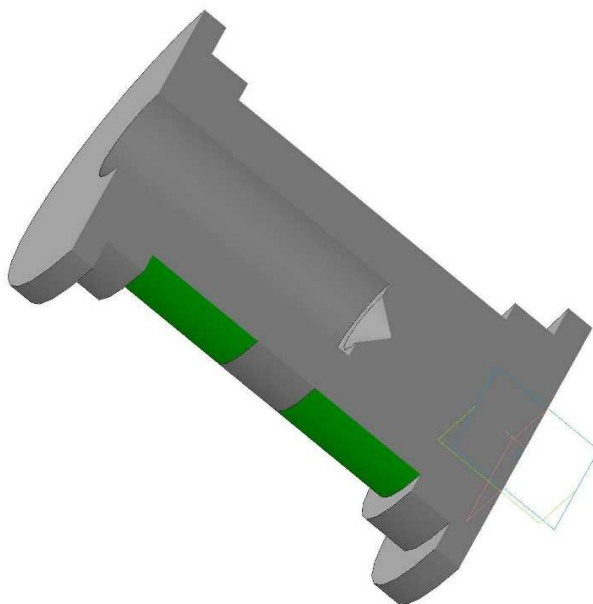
3D-модель части бурового вала с фланцевыми элементами предварительного закрепления и поверхностями трения
